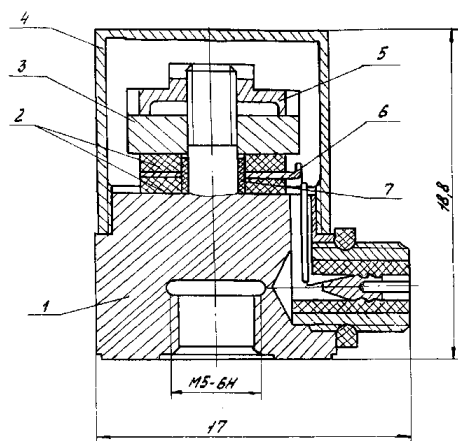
Загальний вигляд віброперетворювача ДН - 4.
